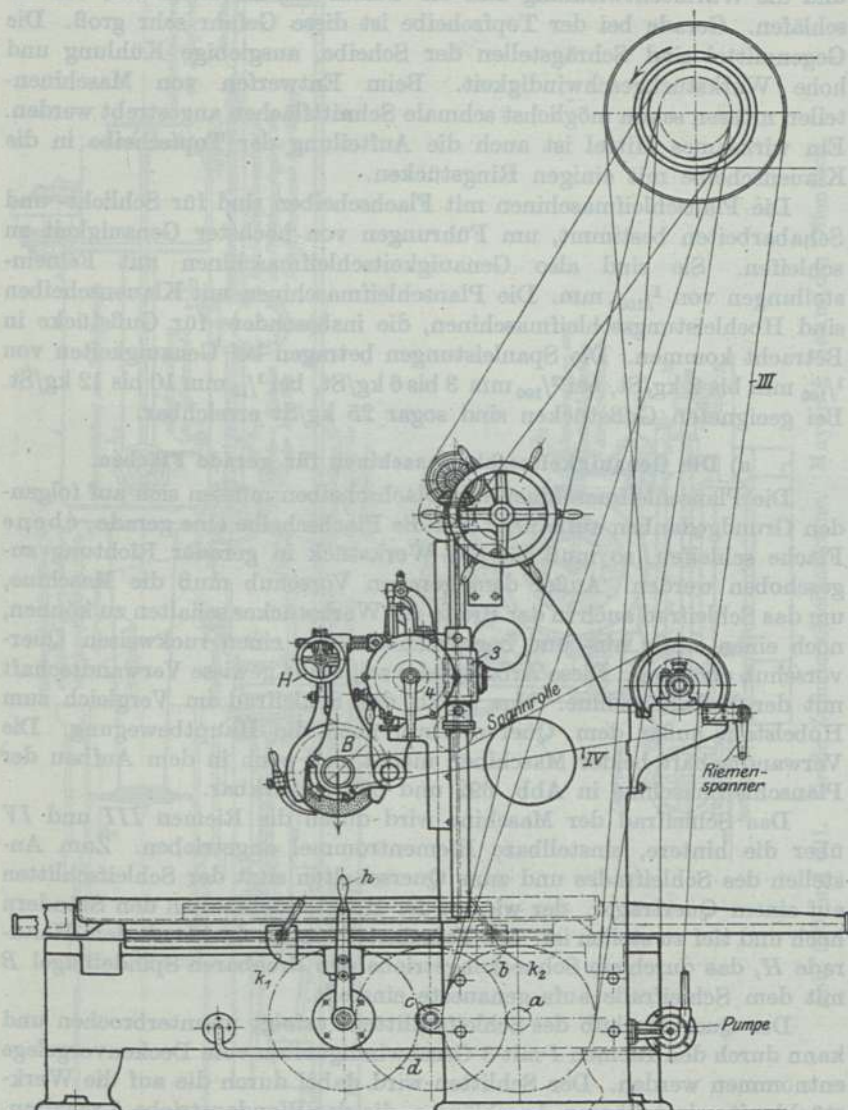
Planschleifmaschine. Fr. Schmaltz, G. m. b. H., Offenbach.
